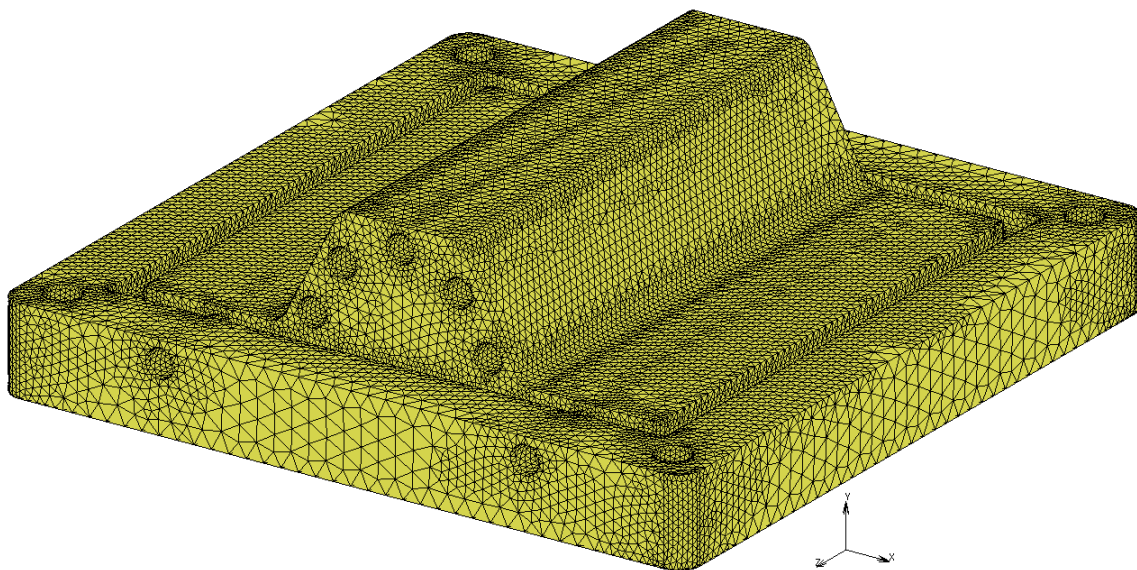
Mallado cuadrático del molde en 3 dimensiones
